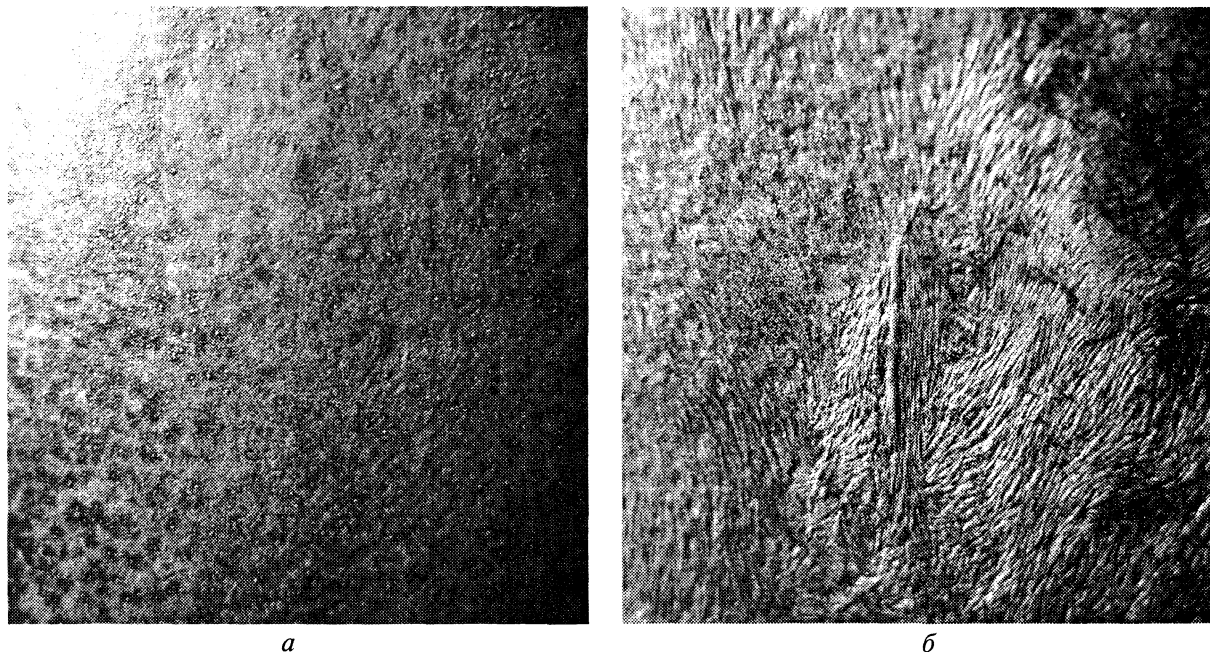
Макроструктура поверхности кокильного литья из сплава АК9: *а* – подвод расплава в кокиль снизу; *б* – верхний подвод металла в кокиль (высота заливки 150 мм). х5. Без травления
